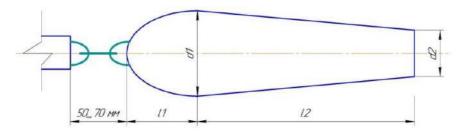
Схема уширителя для кротователя № 3 параболаконической формы Figure 9 — Scheme of expander for mole maker No. 3 of parabolaconic shape
